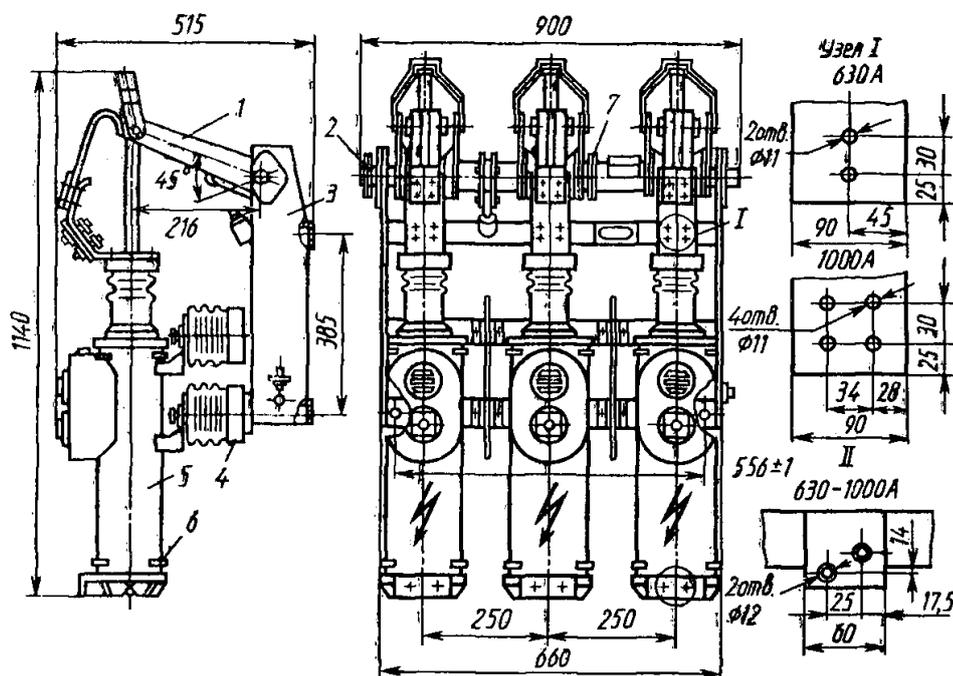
Общий вид выключателя ВМГ-10: 1- изолирующие рычаги; 2 - рычаг бокового присоединения; 3 - рама; 4 - опорный изолятор; 5 - цилиндр (полюс); 6 - съемная крышка; 7 - рычаг среднего присоединения
